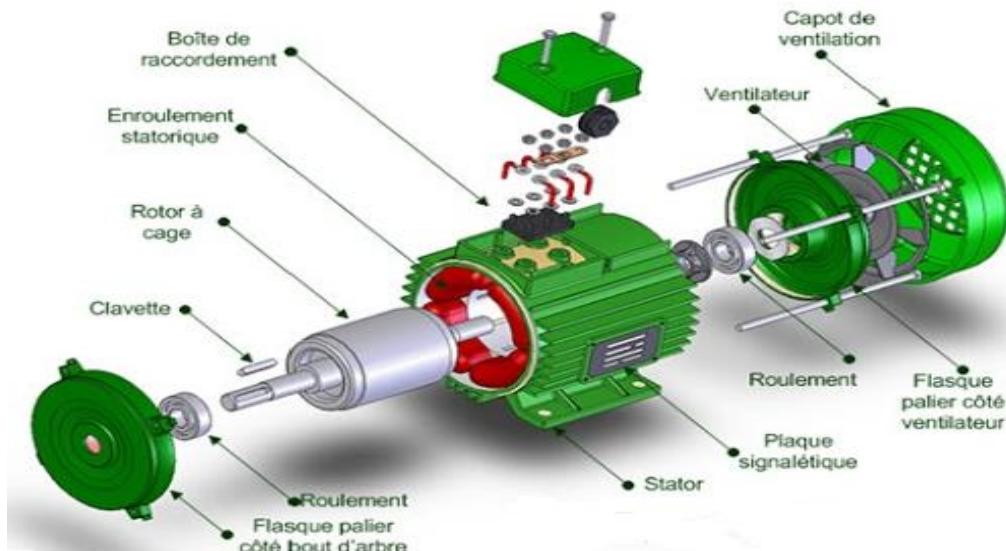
Vue éclatée de la machine asynchrone triphasée à cage
